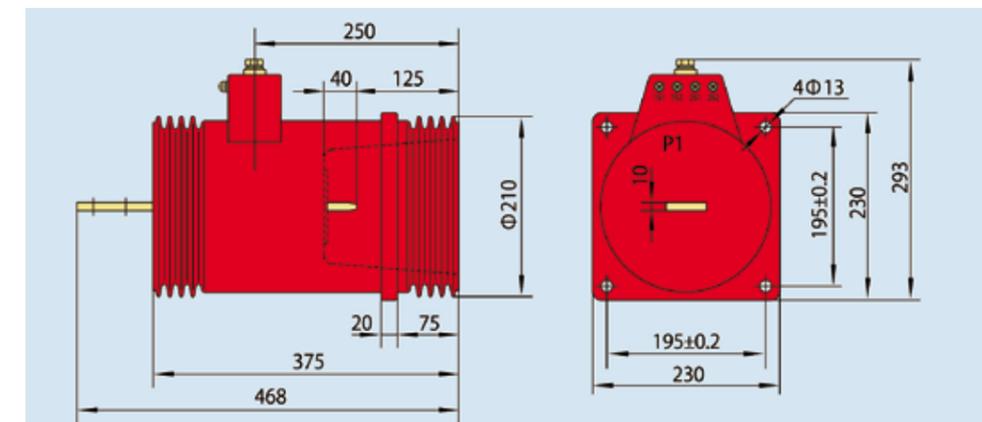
Внешний вид и размеры при 200-1250/5 А
